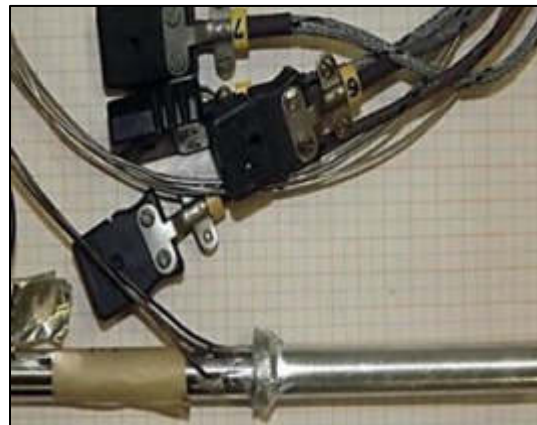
Montaje de materiales para la soldadura de diseño barra con barra [34]
